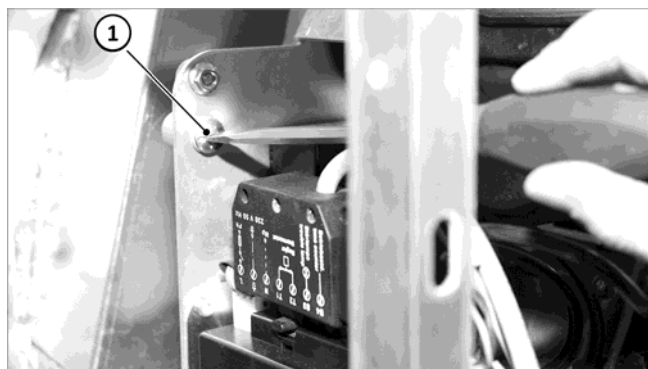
Tornillos de cierre rápido en la unidad del quemador
